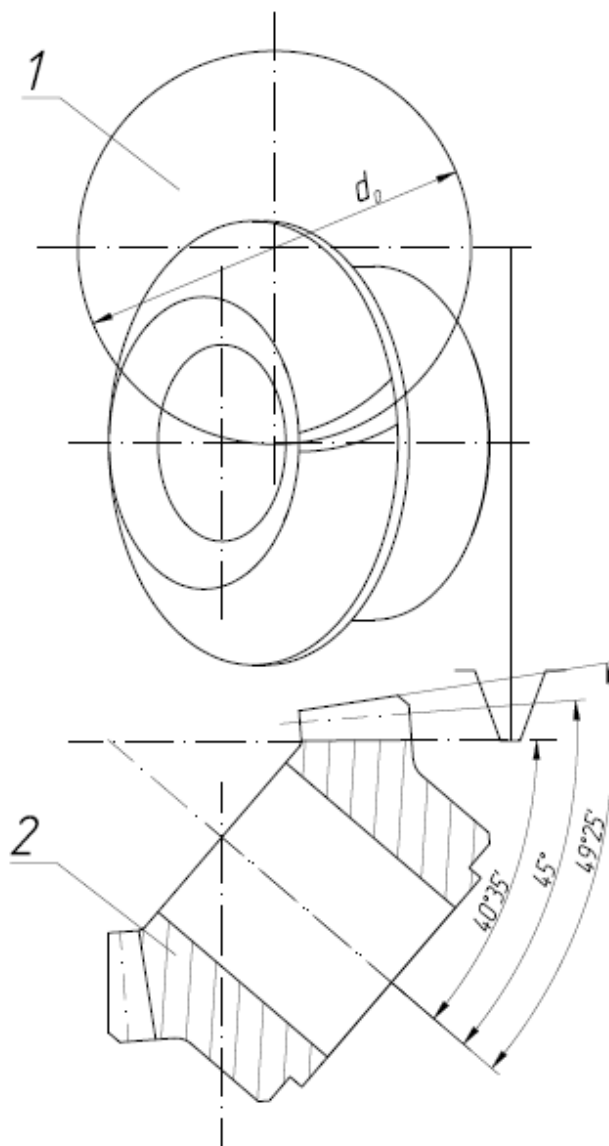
Схема нарезания зуба на коническом зубчатом колесе
